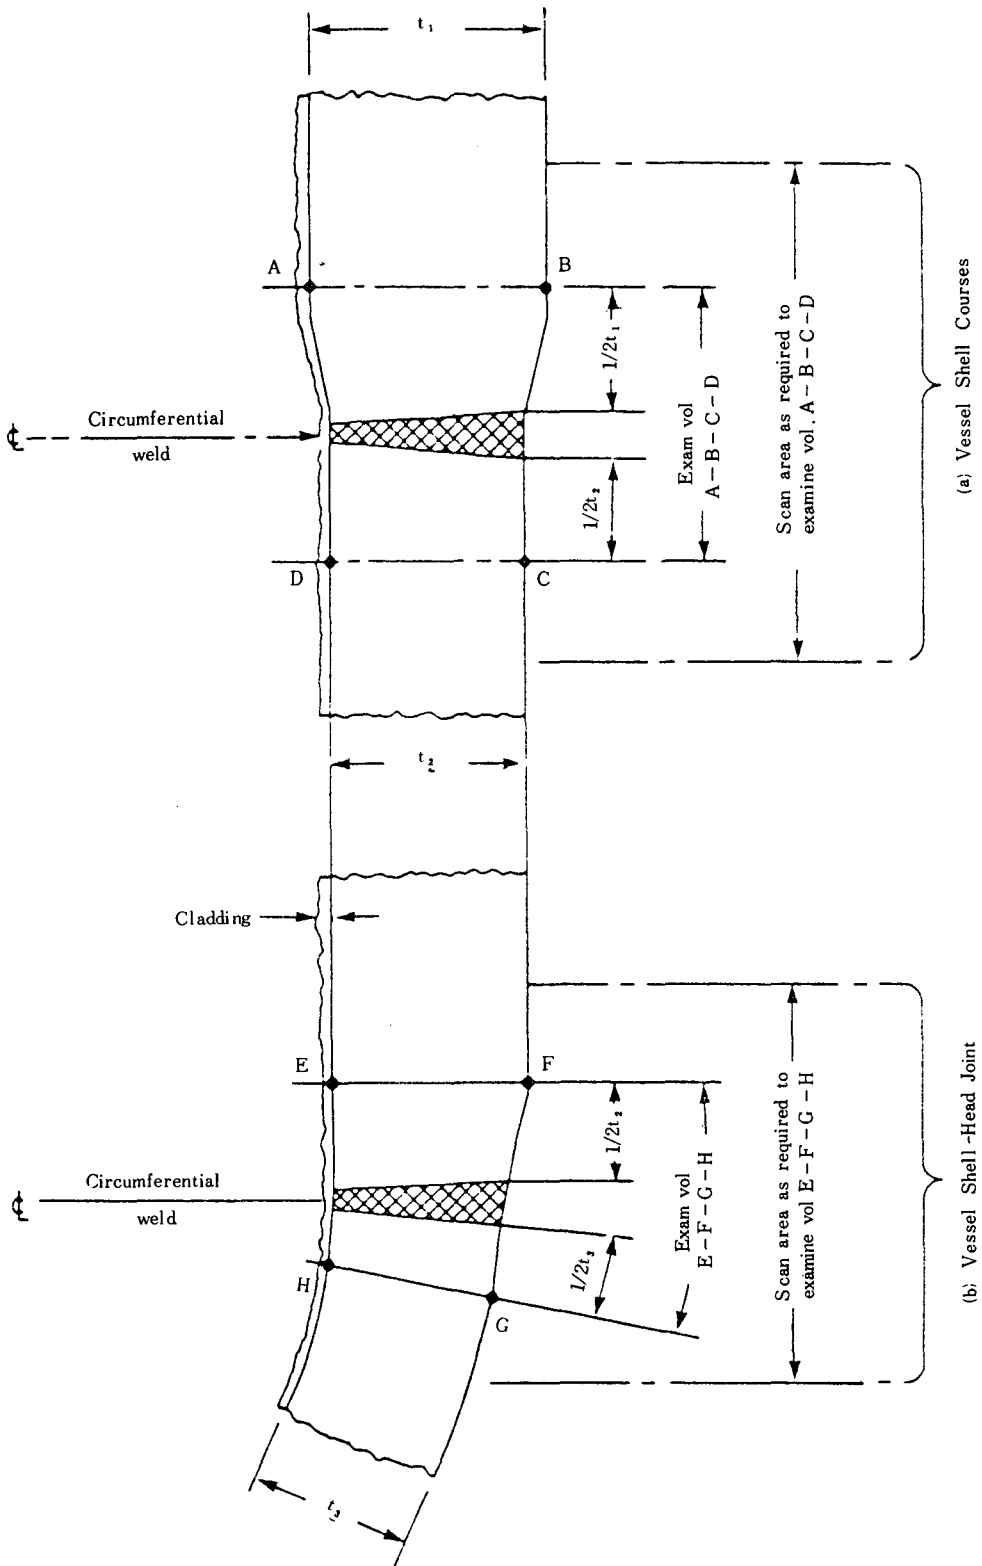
8 VESSEL SHELL CIRCUMFERENTIAL WELD JOINTS
